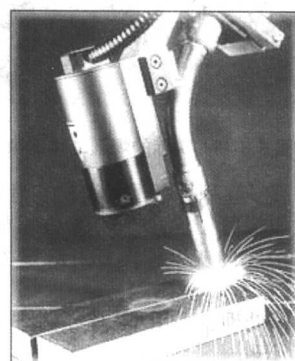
QuickTrack 焊缝跟踪器
